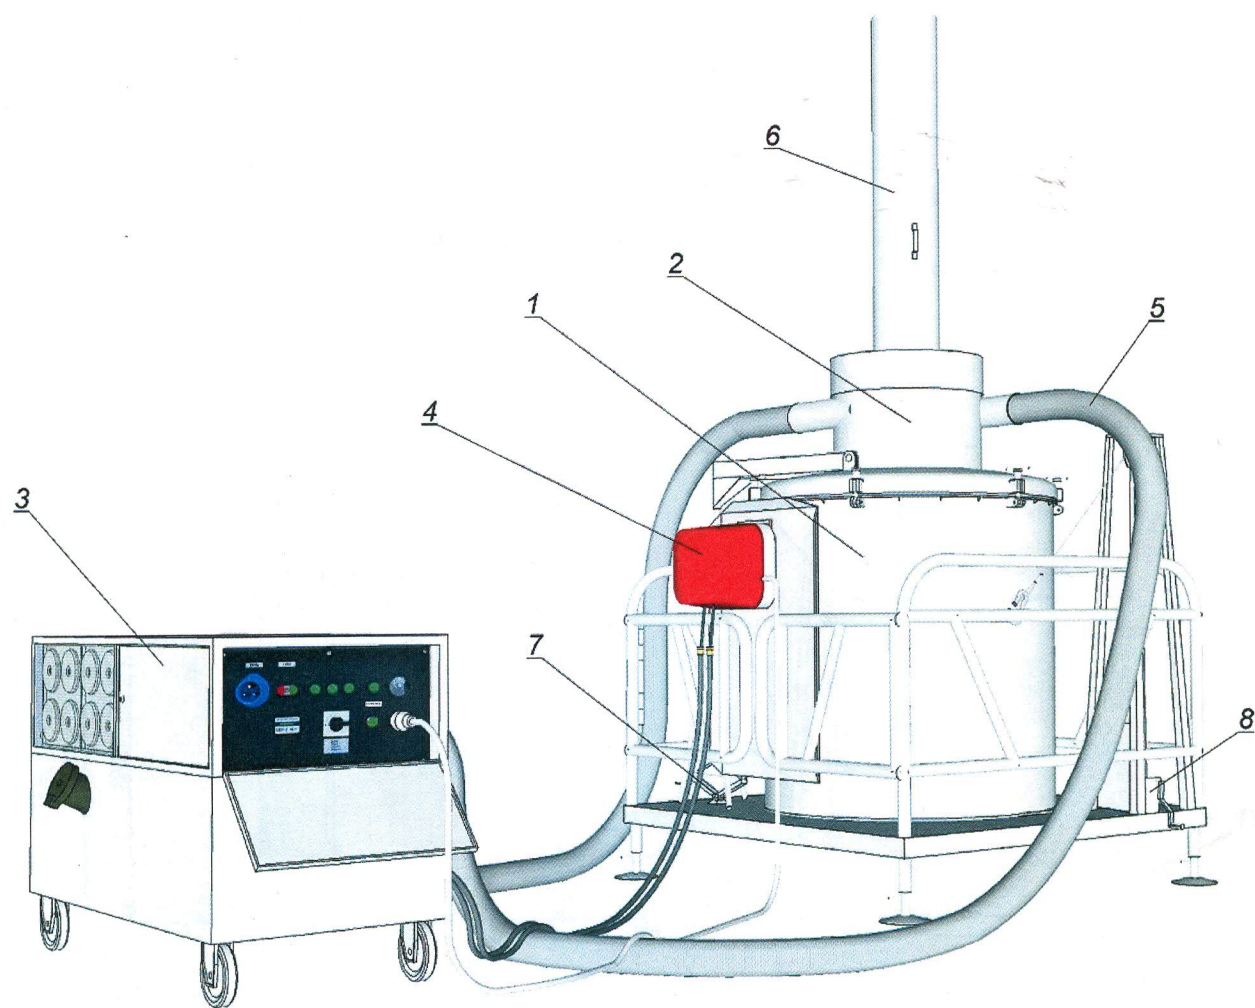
Общий вид установки «Форсаж-2М» в сборе:
